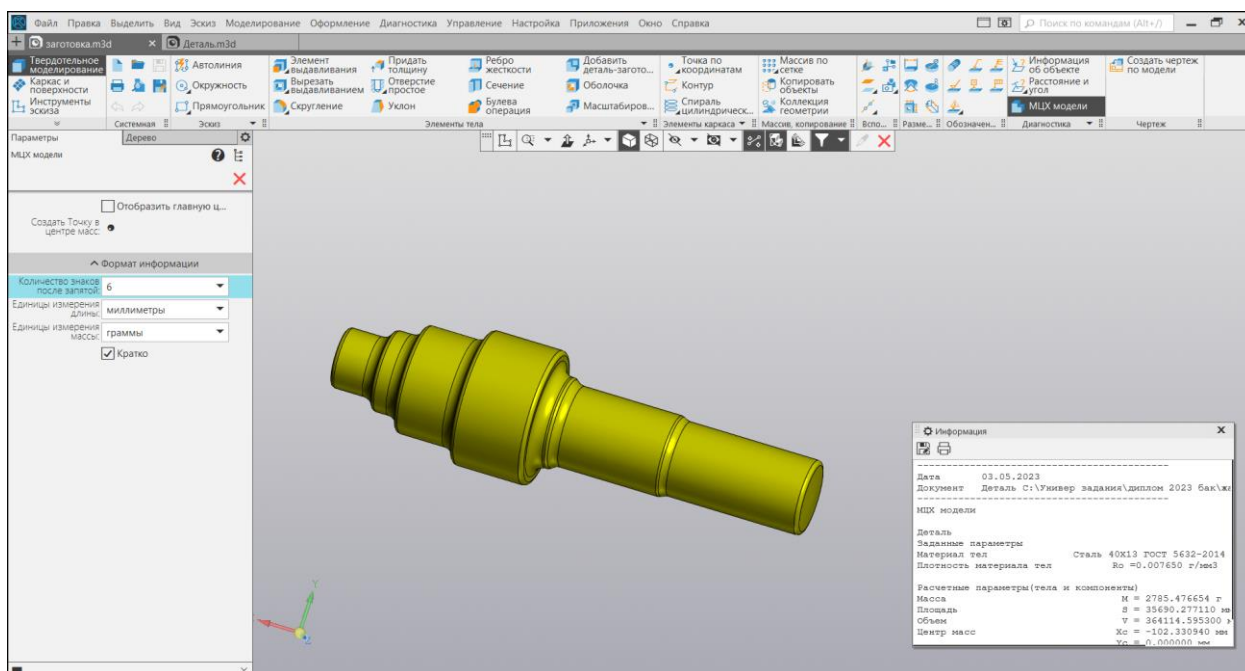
Маса заготовки-штамповки на КГШП
